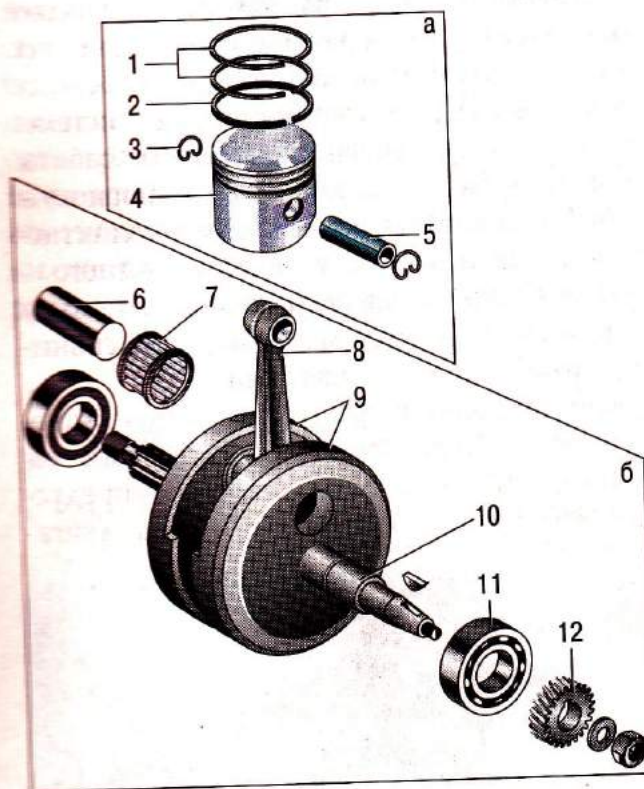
Поршень (а) и коленчатый вал (б) одноцилиндрового четырехтактного двигателя: 1 – компрессионные поршневые кольца; 2 – маслоотъемное кольцо; 3 – кольцо фиксации поршневого пальца; 4 – поршень; 5 – поршневой палец; 6 – шатунная шейка коленчатого вала; 7 – роликовый подшипник нижней головки шатуна; 8 – шатун; 9 – щеки коленчатого вала; 10 – коренная шейка коленчатого вала; 11 – подшипник коленчатого вала; 12 – шестерня моторной передачи
